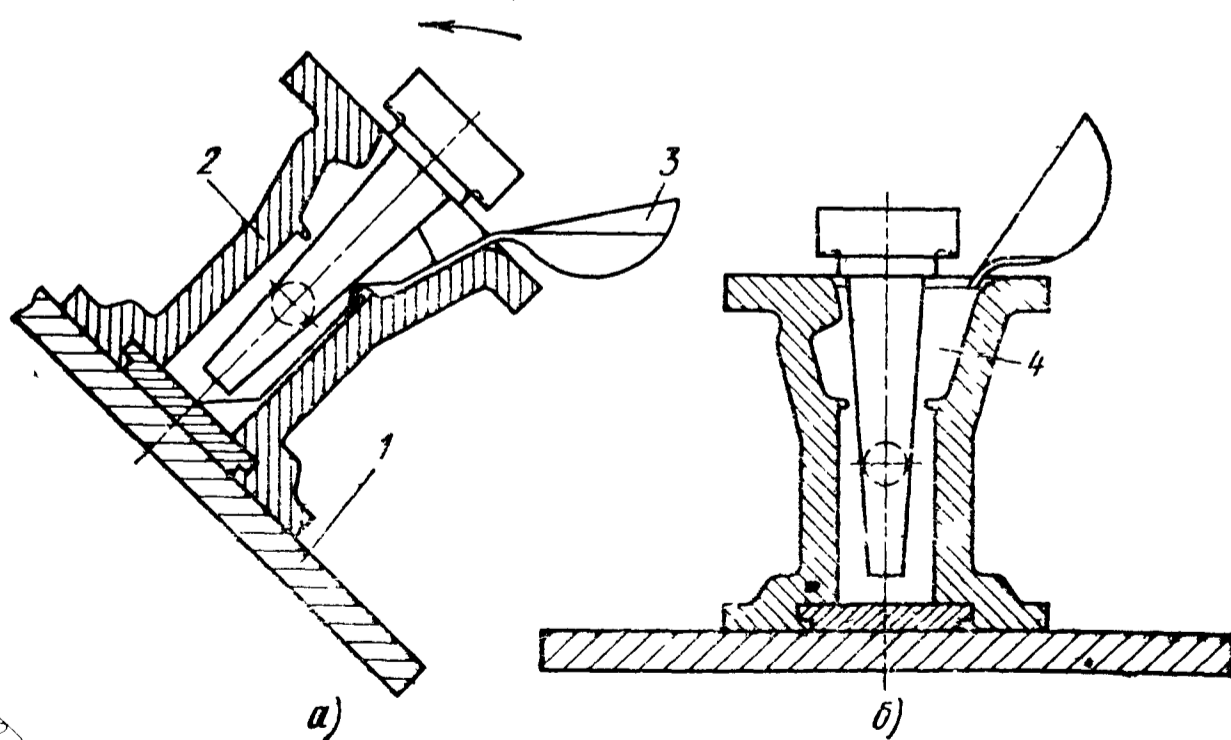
Схема заливки сверху (через прибыль) с кантовкой кокиля (направление поворота указано стрелкой):
